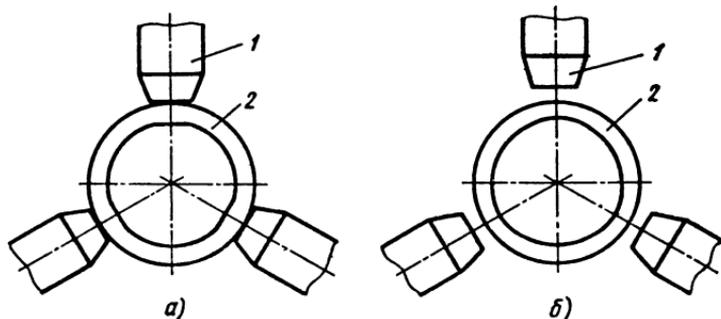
Деформация полого цилиндра при его обработке на токарном станке:
